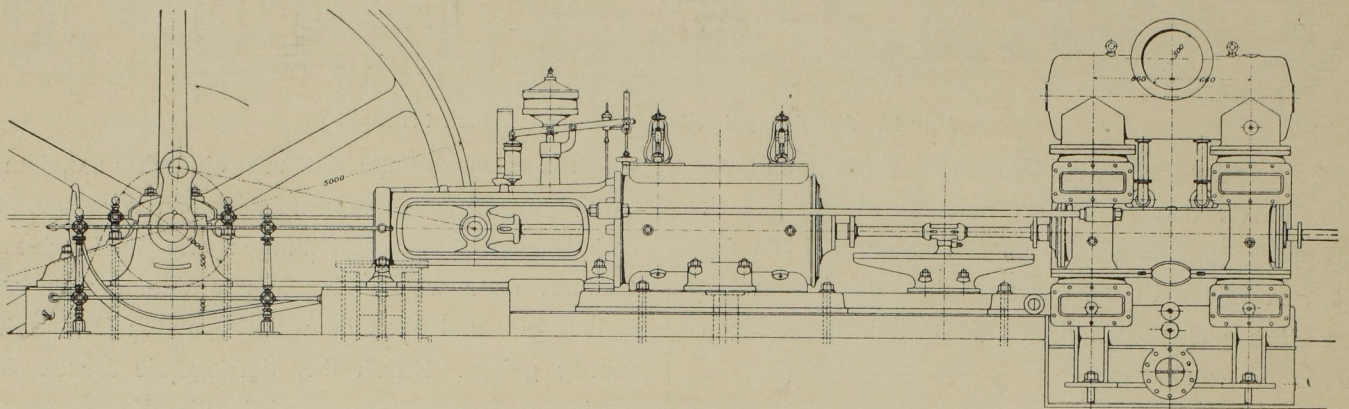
Seitenansicht der Pumpmaschine. Massst. 1 : 60.
